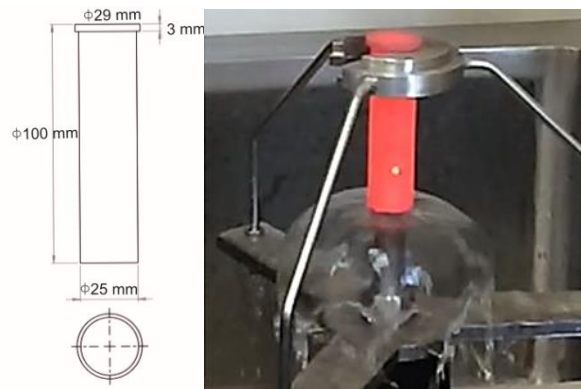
Dimensiones de la probeta y su posición en la ducha de enfriamiento.
